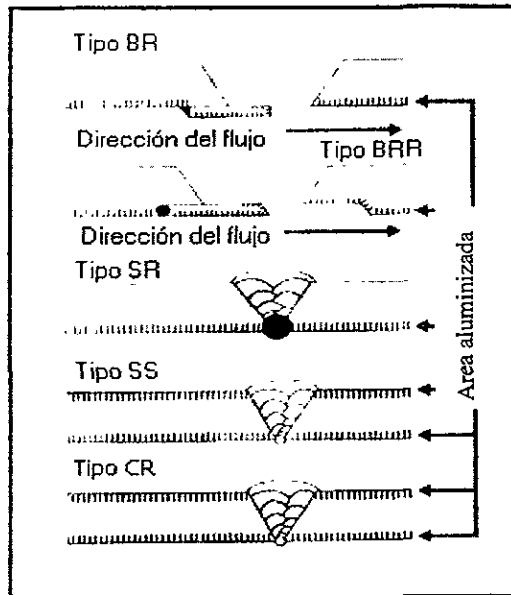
Tipos de juntas soldadas utilizadas en los aceros aluminizados.
